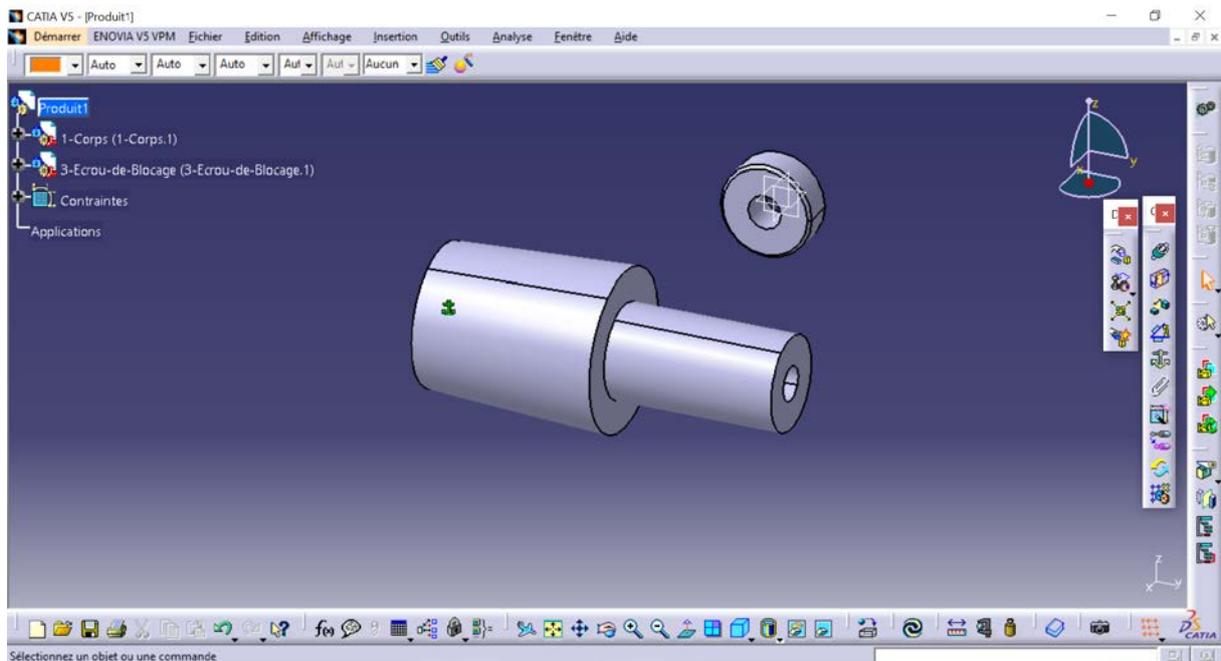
Assembly Design (Insertion de l'Erou de blocage 3) [1], [2]
